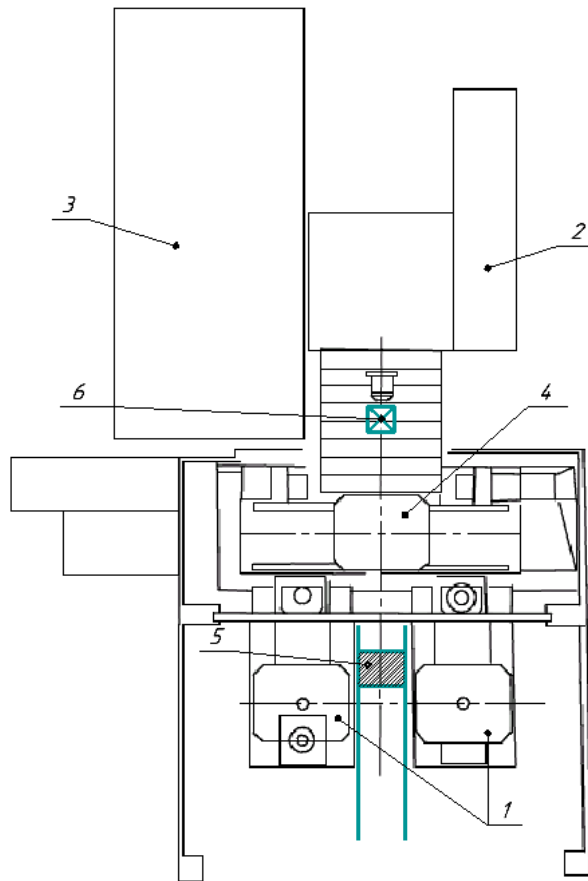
Схема станка с обозначением места для установки робота и местом замены биты, где: 1 – рабочий стол; 2 – силовой шкаф с системой управления; 3 – магазин с приспособлениями для обработки заготовок; 4 – основной рабочий стол; 5 – место расположения робота; 6 – место установки биты
